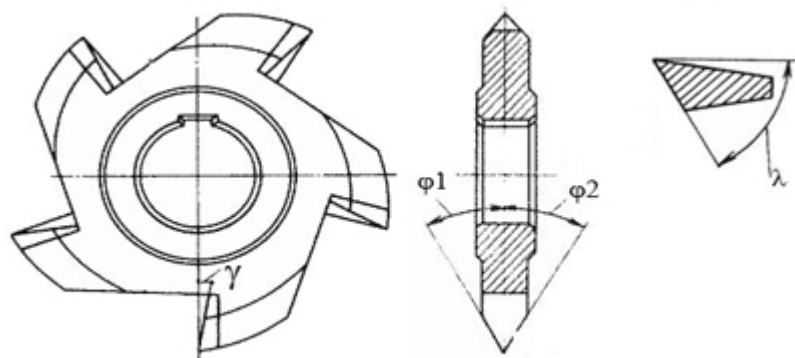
Конструкція дискової обкатної фрези для виготовлення храпових коліс [37,72,80]
